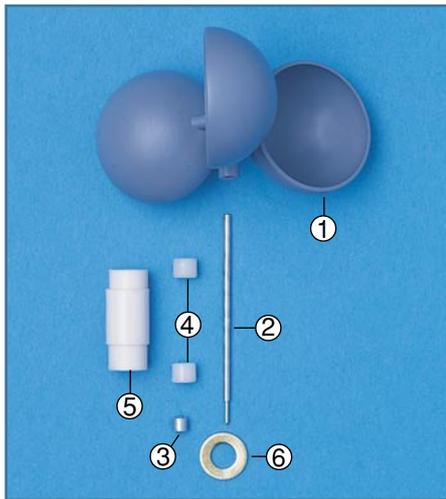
Die mechanischen Einzelteile rund um das Flügelrad.
